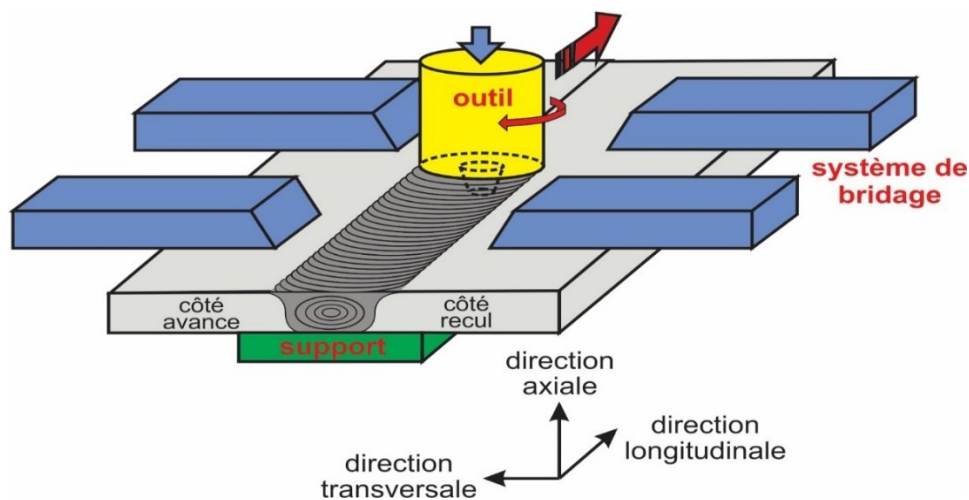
Principales composantes d'une cellule de soudage par friction malaxage (FSW) [9].
